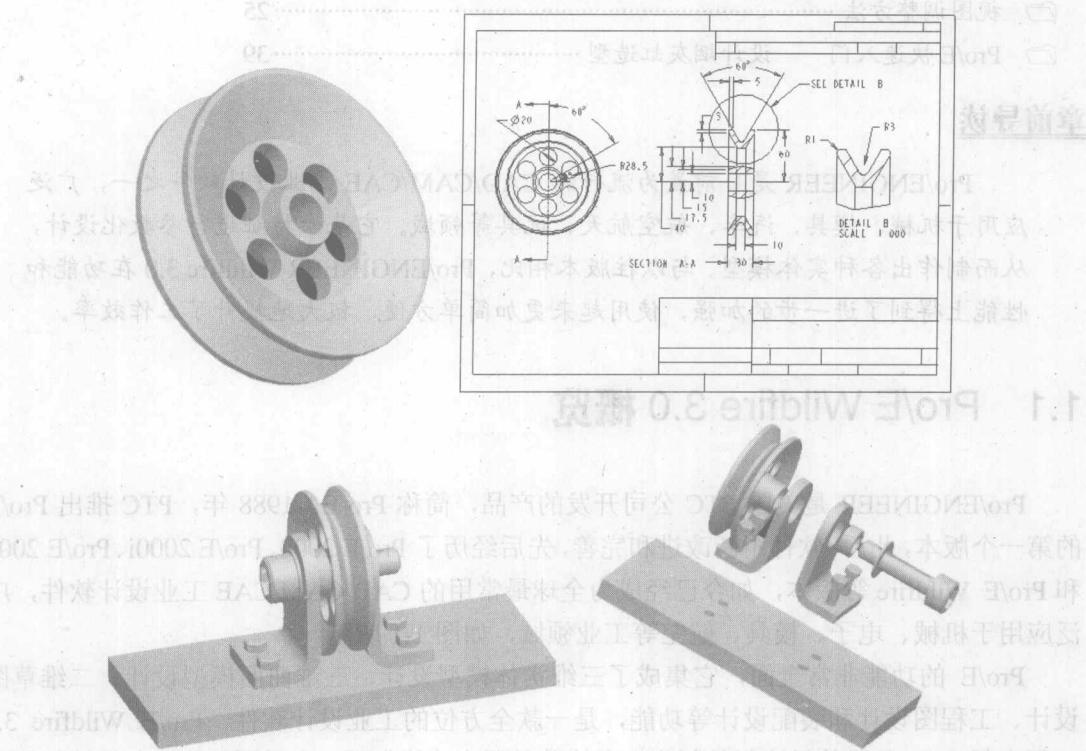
使用 Pro/E 制作的零件图、工程图和装配图
